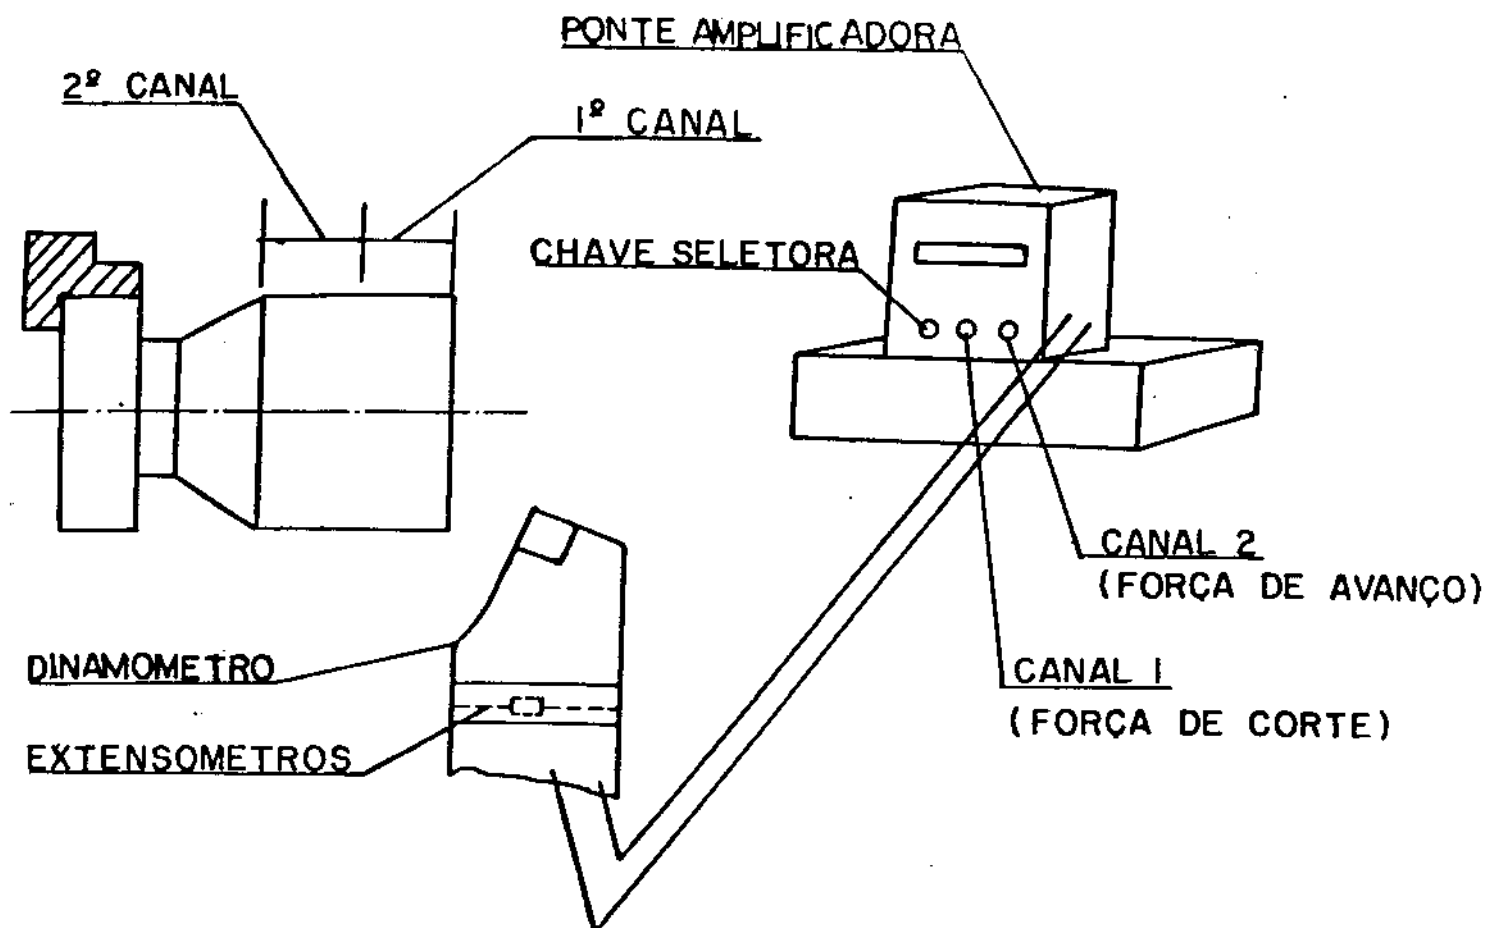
Desenho Esquemático do Método Empregado na Medição das Componentes da Força de Usinagem (Corte & Avanço)
